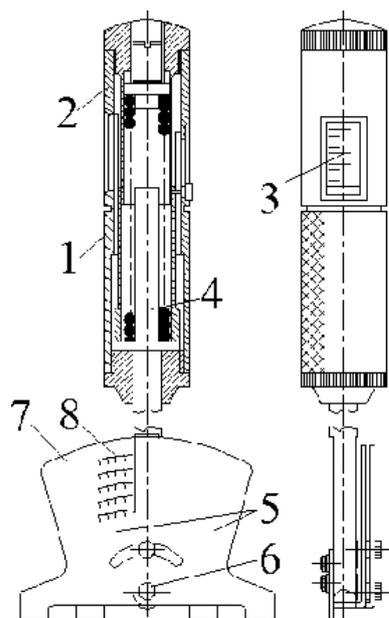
Приспособление КИ - 8920 для проверки натяжения ремней:
